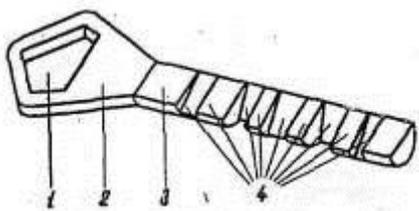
Ключ для замка «Аблой» дискового механизма: 1 - ушко; 2 - головка; 3 - стержень; 4 - уступы
